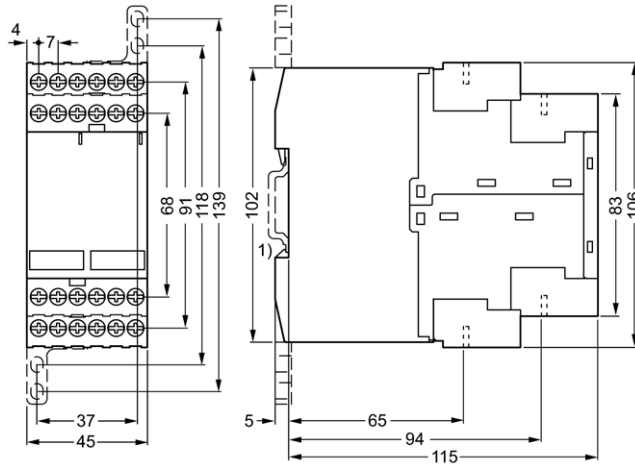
3TK2810/25/26/27/28/34/45 bornes de tornillo
